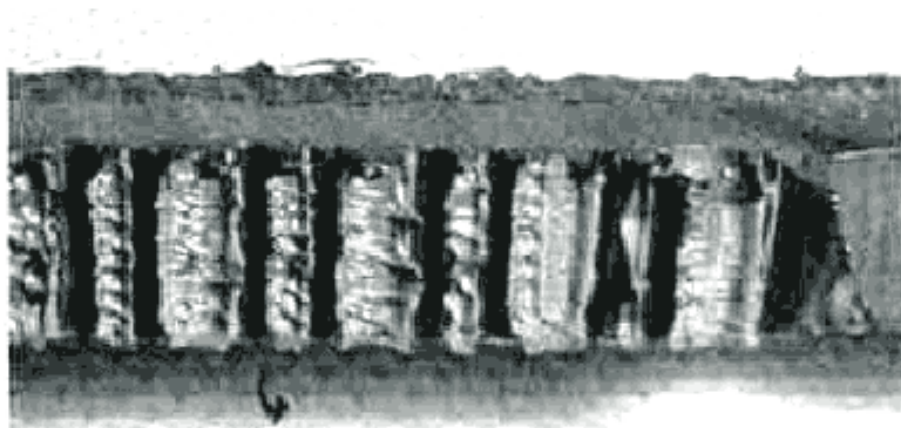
Образец из ПЭ с пластической поверхностью разрушения
